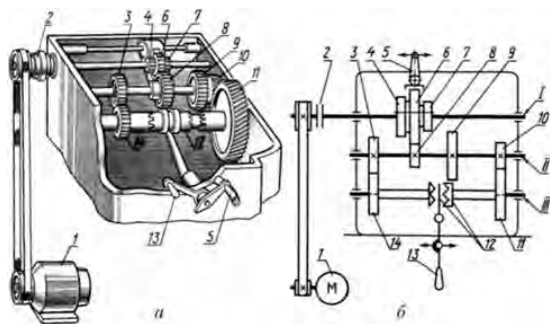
Коробка скоростей токарного станка (а), его кинематическая схема (б)
